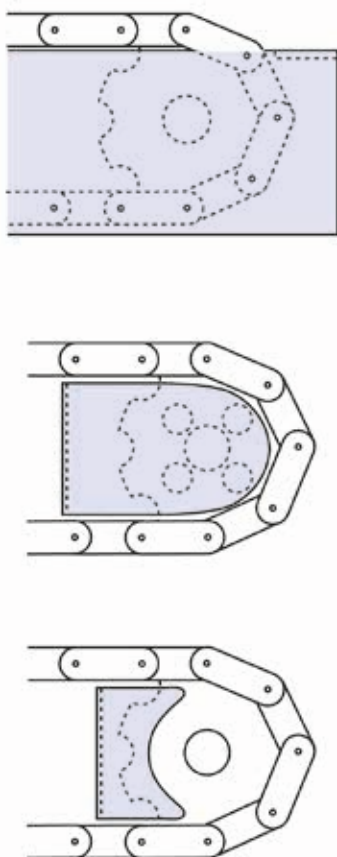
Exemple de protection fixe pour un ensemble chaîne-pignon
